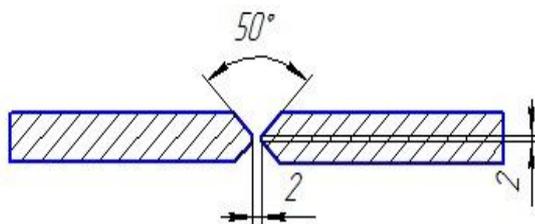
Разделка кромок под электродуговую сварку
